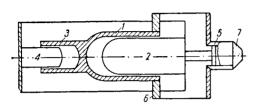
Пресс профильного прессования для термопластичных материалов:
